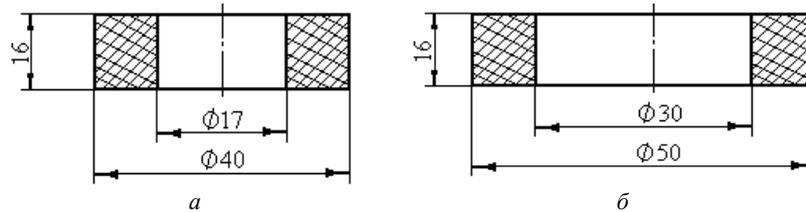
Експериментальний подшипник скользящего дискового сошника универсальной зернотуковкой СЗ-3,6 (а), узла вентилятора овощной сеялки точного высева СУПО-6-01-6 (б)
